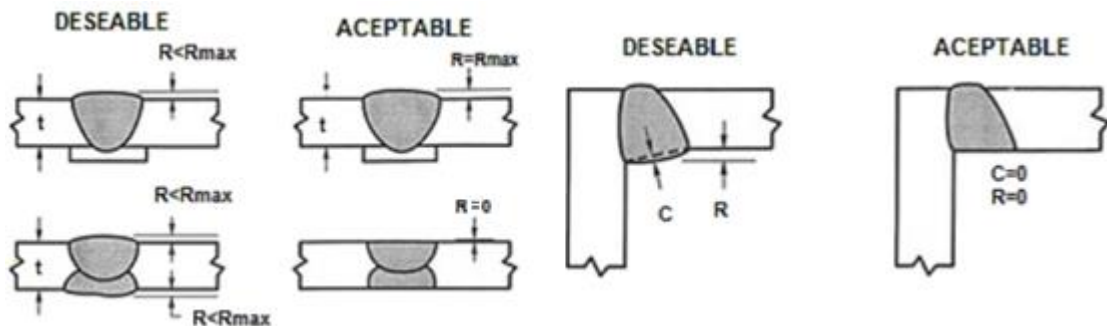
Tamaños y perfiles de soldadura [5].
